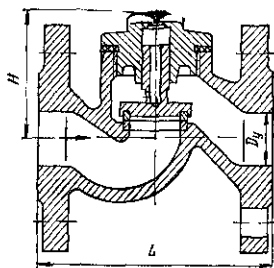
Клапан обратный подъемный фланцевый 16ч3р и 16ч3бр
